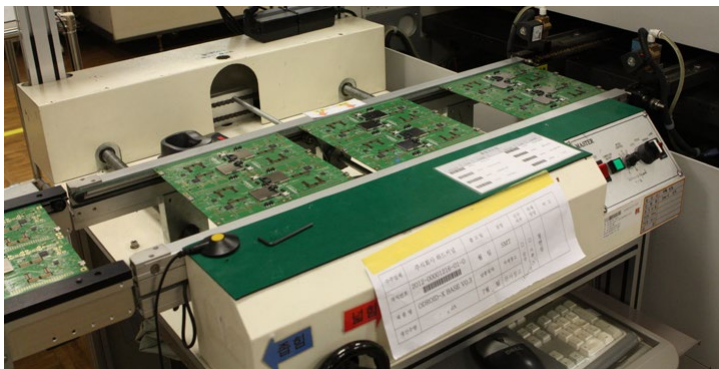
Las placas se introducen en una maquina de soldadura de reflujo.
